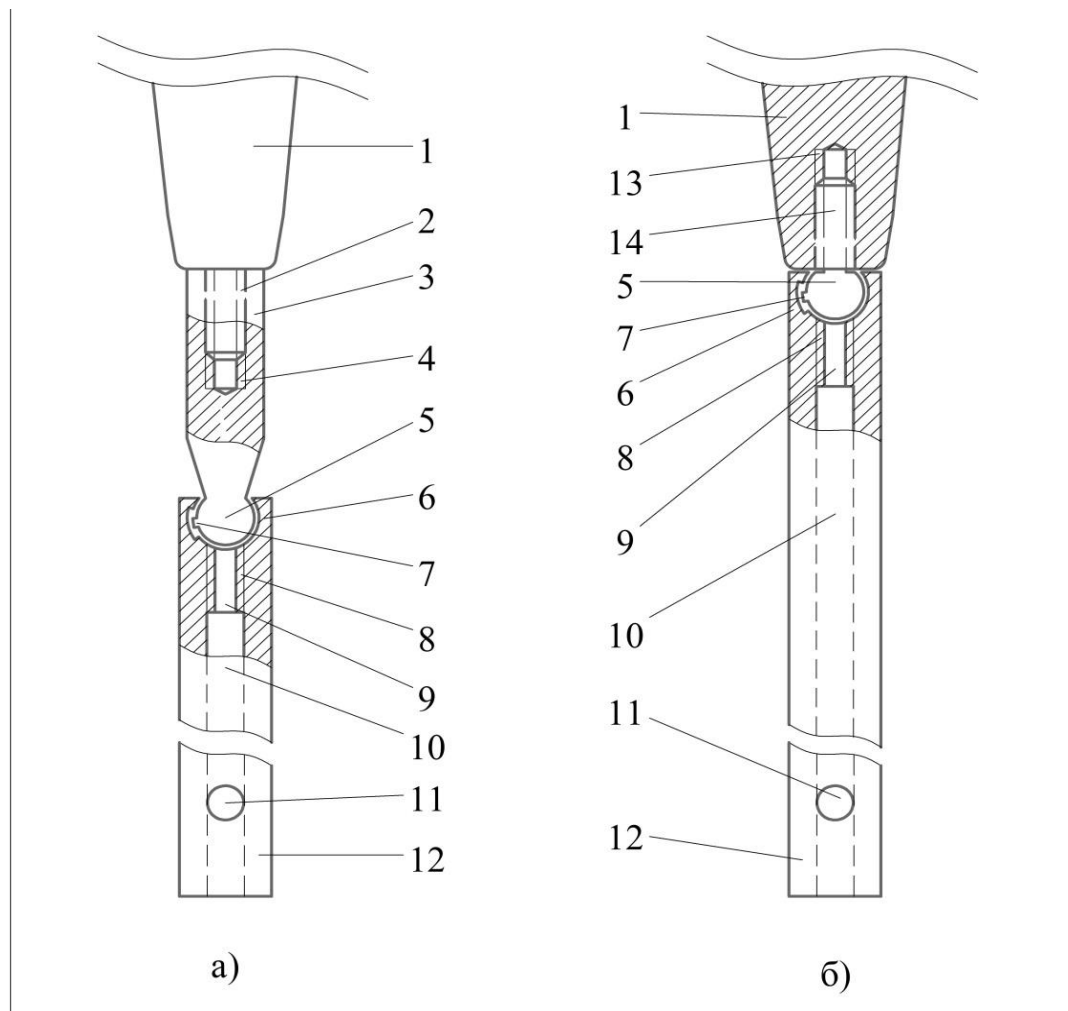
Схема устройства первого комплекта для эндопротезирования тазобедренного сустава: 1 – ножка эндопротеза, 2 – резьба ножки эндопротеза, 3 – верхняя часть штифта, 4 – отверстие с резьбой верхней части штифта, 5 – шарнир, 6 – корпус шарнира, 7 – цилиндрический выступ, 8 – резьба нижней части штифта, 9 – шпилька для фиксации блокирующего механизма, 10 – канал штифта, 11 – отверстие для статического винта, 12 – нижняя часть штифта, 13 – резьба в отверстии ножки, 14 – шпилька с резьбой.
